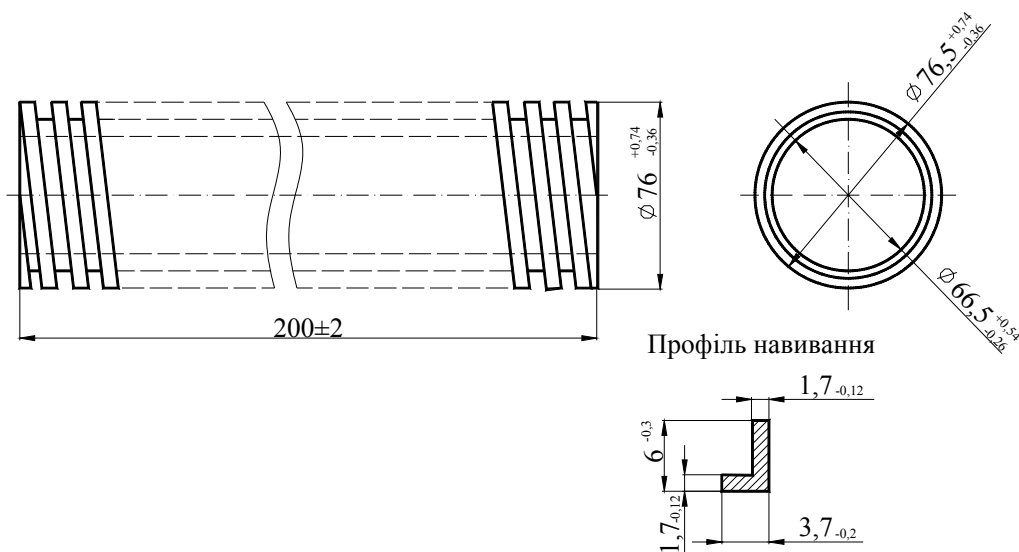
Заготовка гвинтової спіралі для виготовлення стопорних кілець з горизонтальними полицками
